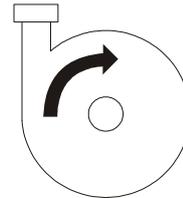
Drehrichtung einer hydraulischen Kreiselpumpe
